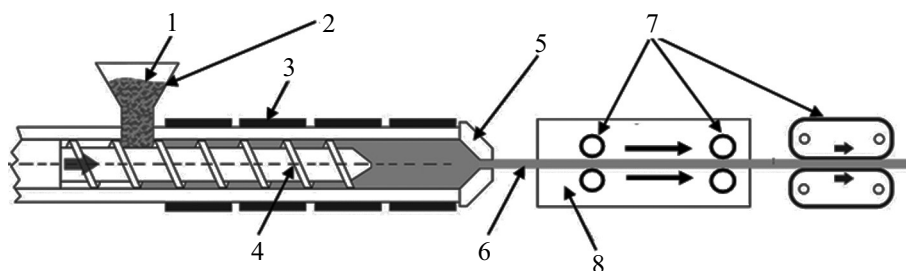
Изготовление композитов методом экструзии: 1 — гранулы сырья; 2 — дозатор; 3 — нагревающие элементы; 4 — червяк; 5 — фильера; 6 — композитный материал; 7 — эскалаторы; 8 — охлаждающая камера.
